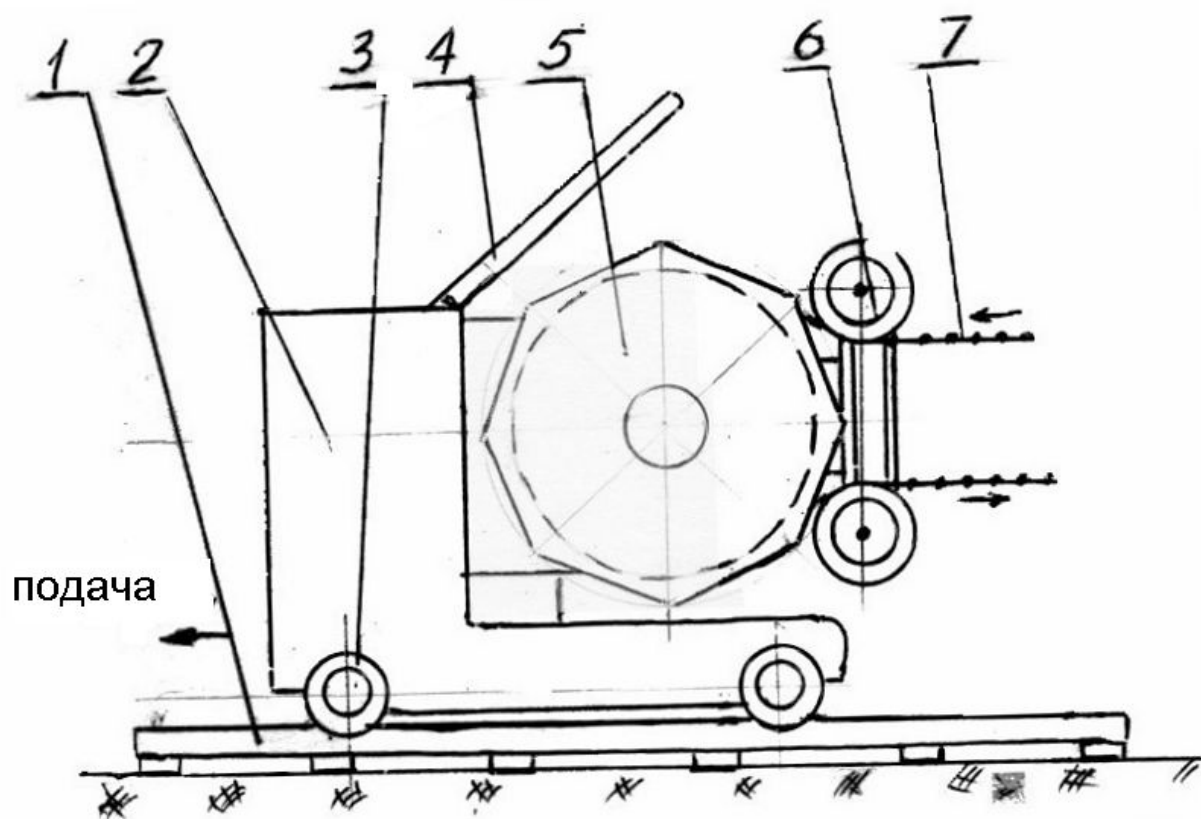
Принципиальная схема алмазно-канатной добычной установки. 1-рельсовый путь; 2-корпус; 3-колеса; 4-защитная планка (защита от оборванного каната);5-поворотный узел с рабочим (приводным) шкивом; 6- вспомогательные направляющие шкивы; 7-алмазный канат.
